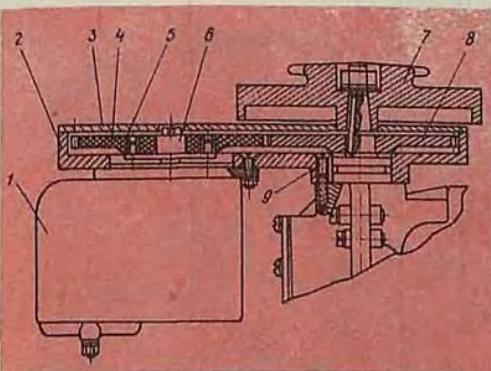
Установка магнето М-47Б: 1 — магнето; 2 — корпус редуктора; 3 — крышка редуктора; 4 — шестерня; 5 — резиновая втулка; 6 — муфта; 7 — маховик; 8 — шестерня; 9 — винт крепления корпуса редуктора.
